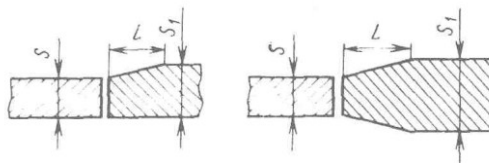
Подготовка кромок при сварке элементов различной толщины
